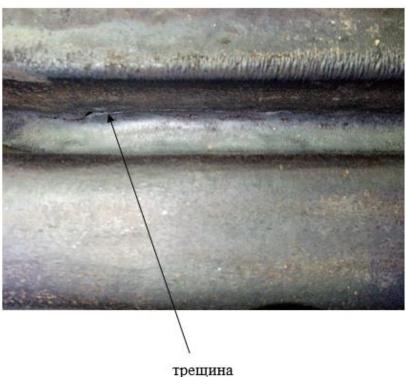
Общий вид поверхности изношенной рабочей гравюры штампа с наличием трещины
